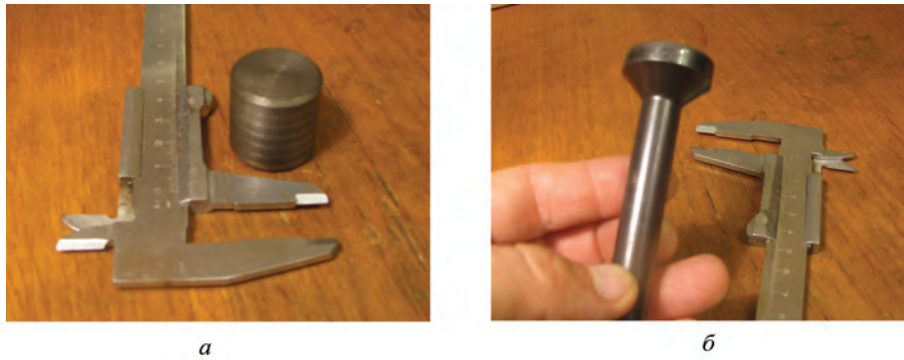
Общий вид исходной заготовки из высокопрочного чугуна ВЧ50 (а) и полученного горячим выдавливанием деформированного прутка (б)
